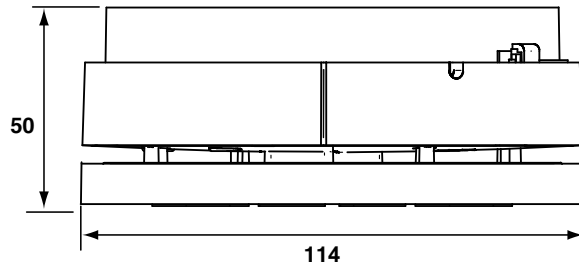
FC430LPBSB LP Sirena/lampeggiatore con flangia di montaggio— Dimensioni generali
